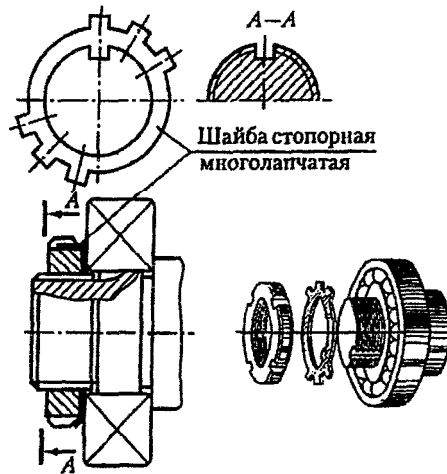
Круглая шлицевая гайка со стопорной многолопчатой шайбой
